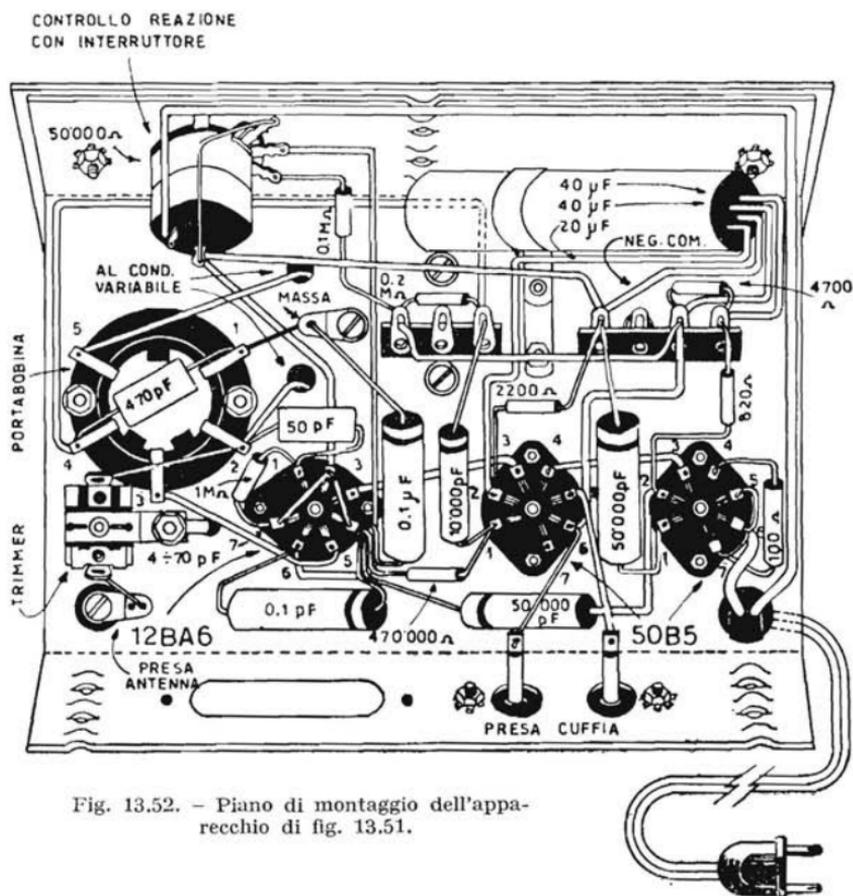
Piano di montaggio dell'apparecchio di fig. 13.51.
